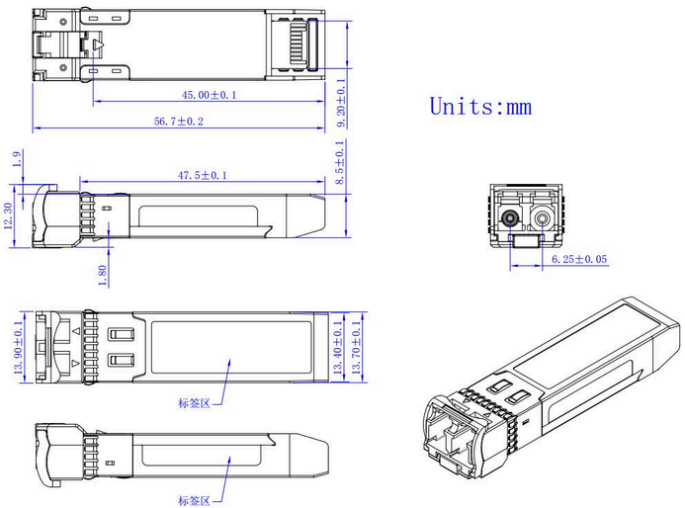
Desenho Técnico e Dimensões Mecânicas (em milímetros)
